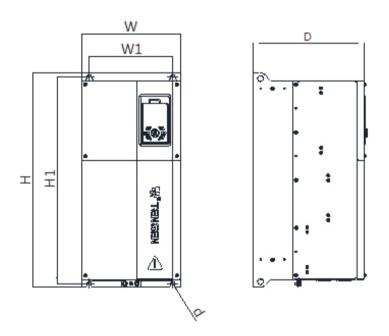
Габаритный чертеж типа F, типа G, типа H, типа I, типа J
